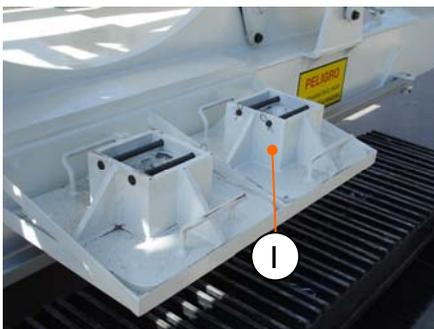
Vista-Leyenda detalles del Elevador Móvil
